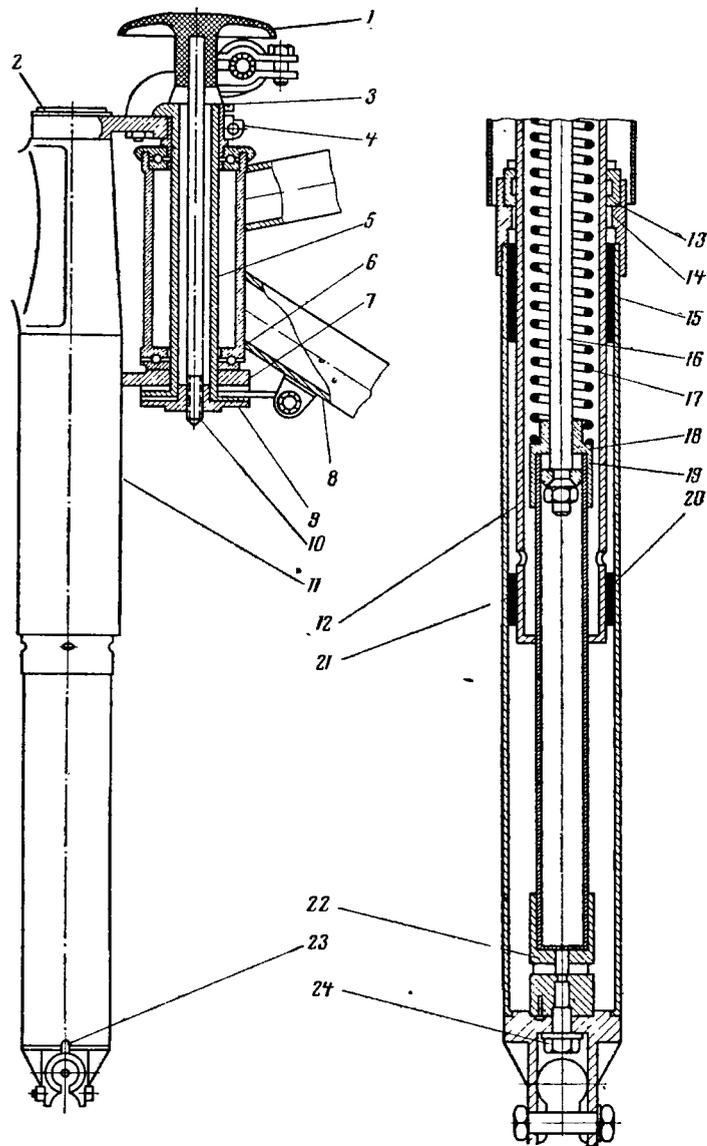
Передняя вилка мотоцикла ИЖ-56: 1 — рукоятка демпфера; 2 — пробка; 3 — пружина; 4 — верхний мостик; 5 — стержень; 6 — подшипник; 7 — нижний мостик; 8 — рама; 9 — диск демпфера; 10 — шпилька; 11 — кожух; 12 — трубка; 13 — корпус сальника; 14 — сальник; 15 — текстолитовая втулка; 16 — шток; 17 — пружина; 18 — крышка; 19 — поршень; 20 — бронзовая втулка; 21 — трубка; 22 — скользящая трубка; 23 — корпус; 24 — пробка.
